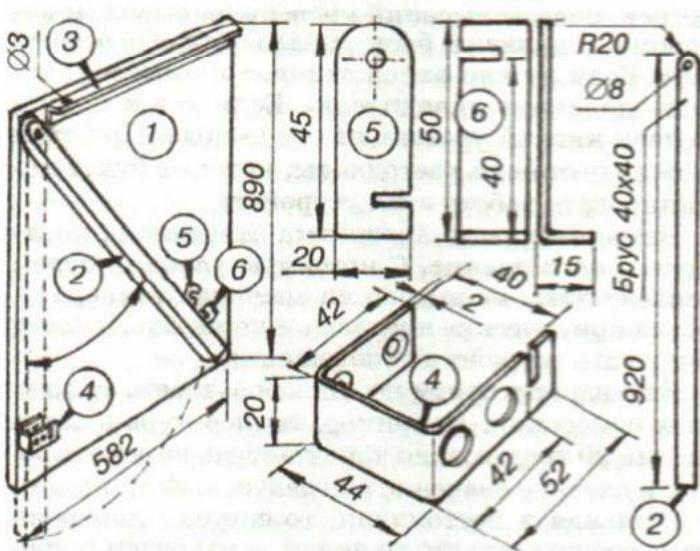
Детали левой створки: 1 — створка; 2 — стойка (ножка); 3 — опорный уголок с отверстием для штифта; 4 — фиксатор; 5 — скоба фиксатора; 6 — уголок скобы.
